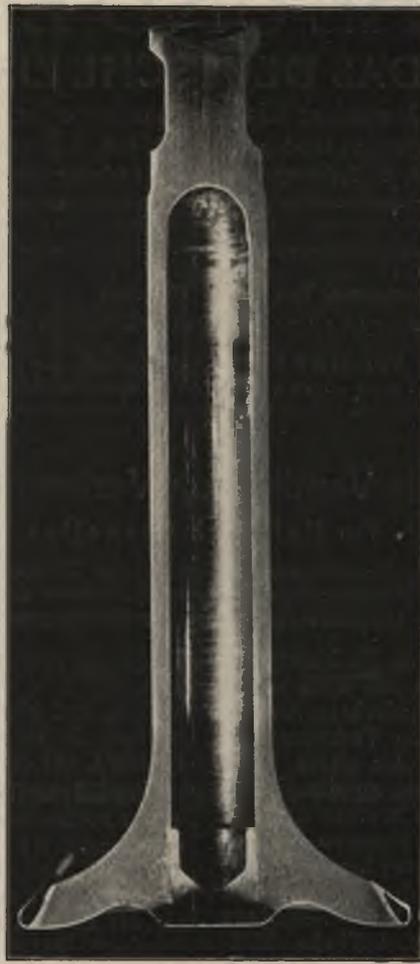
Hohlshaft-Auslaßventil mit eingeschweißtem Stopfen im Tellerboden aus einem deutschen Flugmotor. (× rd. 1.)
